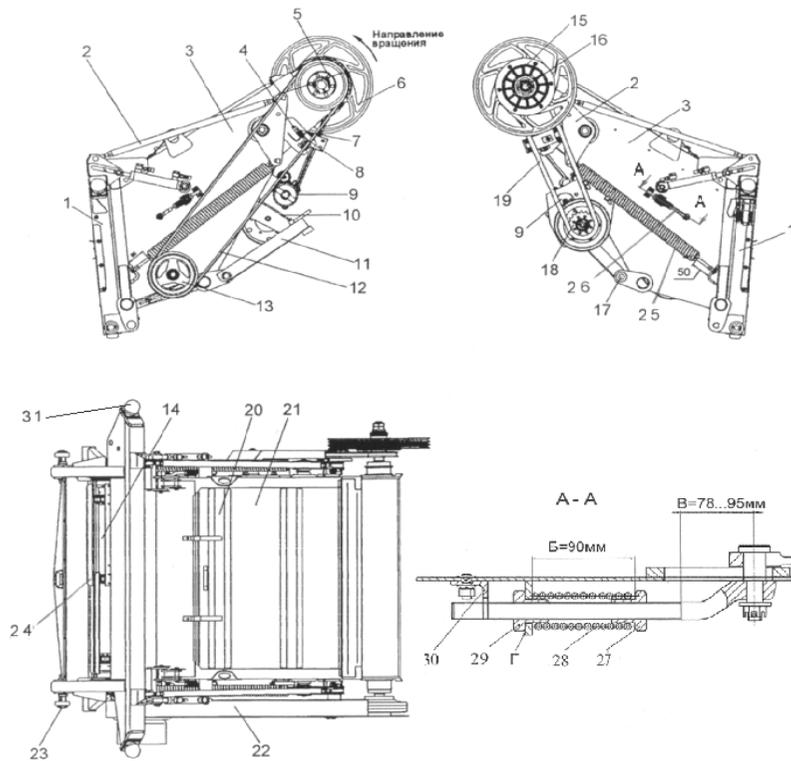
Наклонная камера: 1 — рамка переходная; 2 — механизм продольного копирования; 3 — рама; 4 — крюк; 5, 6, 13 — шкивы; 7 — пружина; 8, 27, 29 — гайки; 9 — стартер; 10 — подвес; 11 — упор; 12 — передача ременная от верхнего вала к контрприводу; 14 — вал нижний; 15 — муфта предохранительная; 16 — вал верхний; 17 — палец; 18 — звездочка; 19 — передача цепная механизма реверса; 20, 22 — ограждения; 21 — крышка; 23 — эксцентрик с упорным роликом; 24 — транспортер цепочно-планчатый; 25 — пружина; 26 — устройство для натяжения транспортера; 28 — пружина; 30 — уголок; 31 — ролик шаровой
